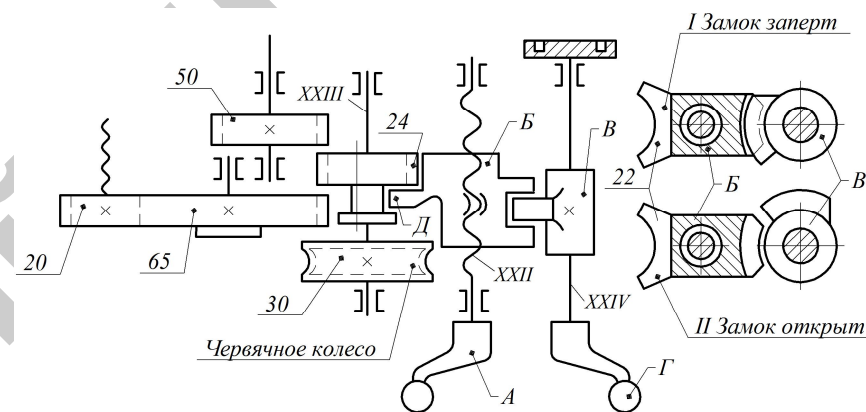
Блокировочный механизм токарно-винторезного станка 1А62
